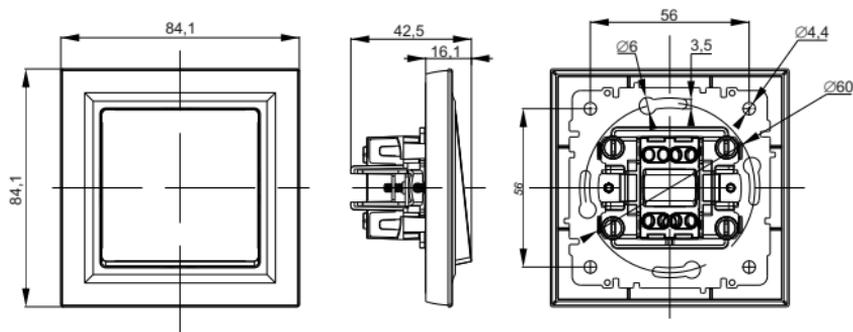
Габаритные и установочные размеры выключателей с рамкой / Figure 3 – Overall and mounting dimensions of switches with frame / 3-сурет – Жақтауы бар ажыратқыштардың габаритті және орнату өлшемдері / Рисунок 3 – Габаритні та установчі розміри вимикачів з рамкою / Attēls 3 – Slēdžu ar rāmi gabarīta un uzstādīšanas izmēri / Pav. 3 – Jungkliķi īsmatavimai ir montavimo dydžiai su rėmeliu / Joonis 3 – Raamiga lülitite üld-ja paigaldusmõõtmed / Figura 3 – Dimensiunile și dimensiunile de instalarea a comutatoarelor cu cadru / Bild 3 – Haupt- und Anschlussabmessungen der Schalter mit einem Rähmchen
